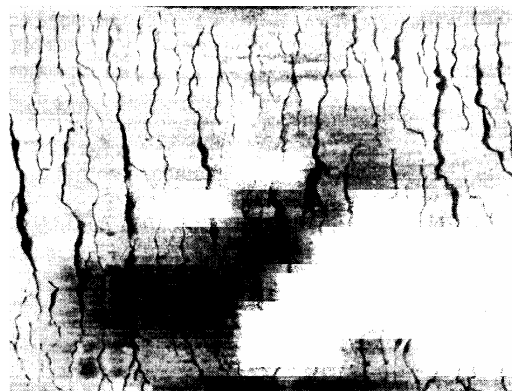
Поверхность подшипника двигателя, залитого свинцовой бронзой, с усталостными повреждениями в виде сетки трещин
